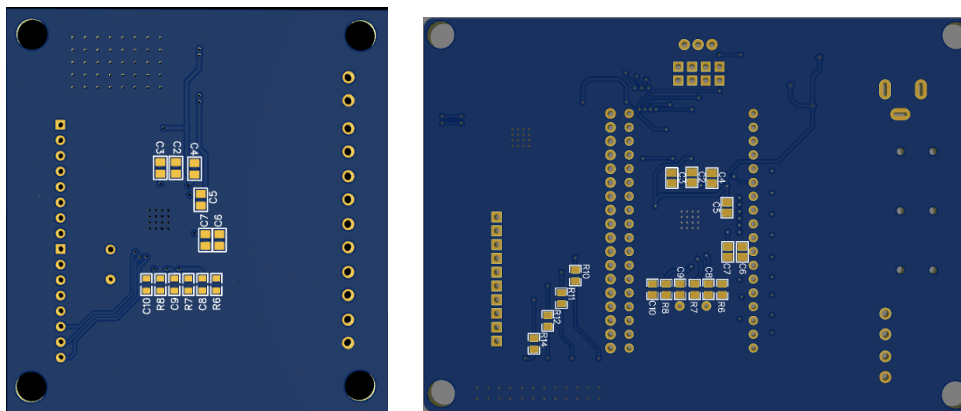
Capa Bottom PCB V1.0 y V2.0. Fuente propia.
